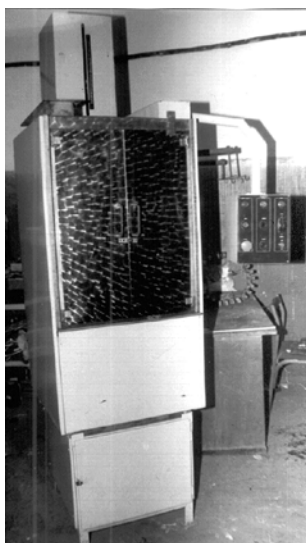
Внешний вид установки ЭРОМ-114
